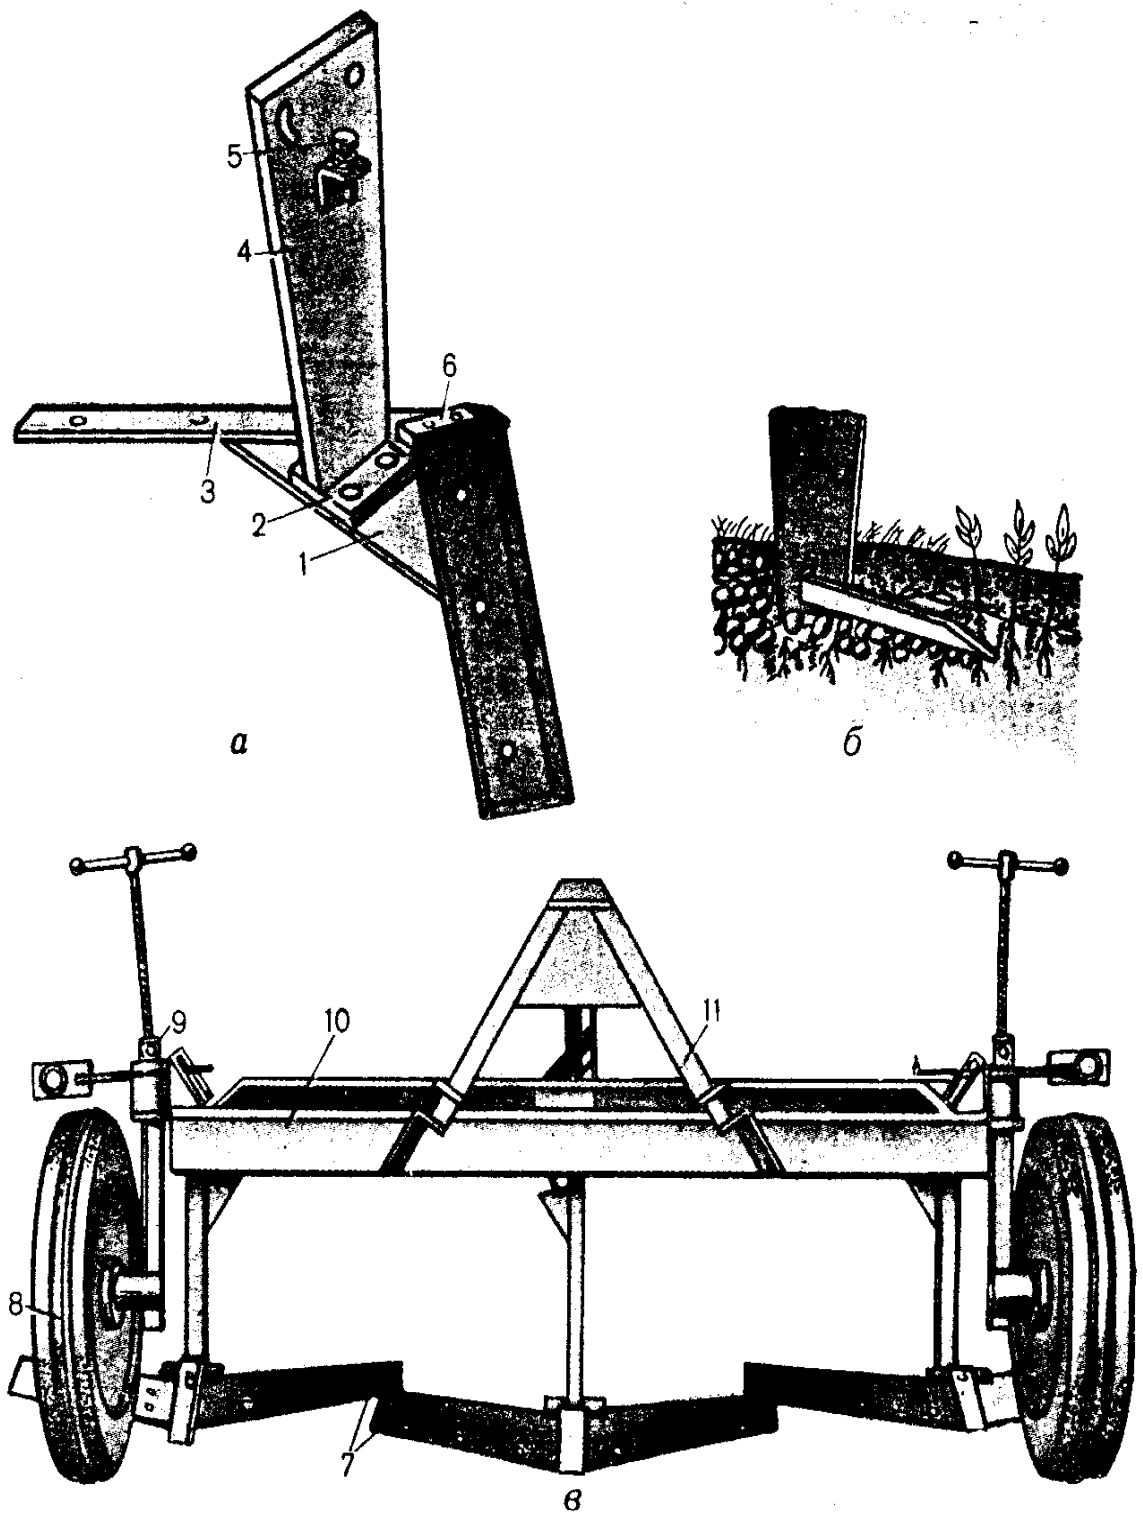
Плоскорез-глубококорыхлитель ПГ-3-100:
